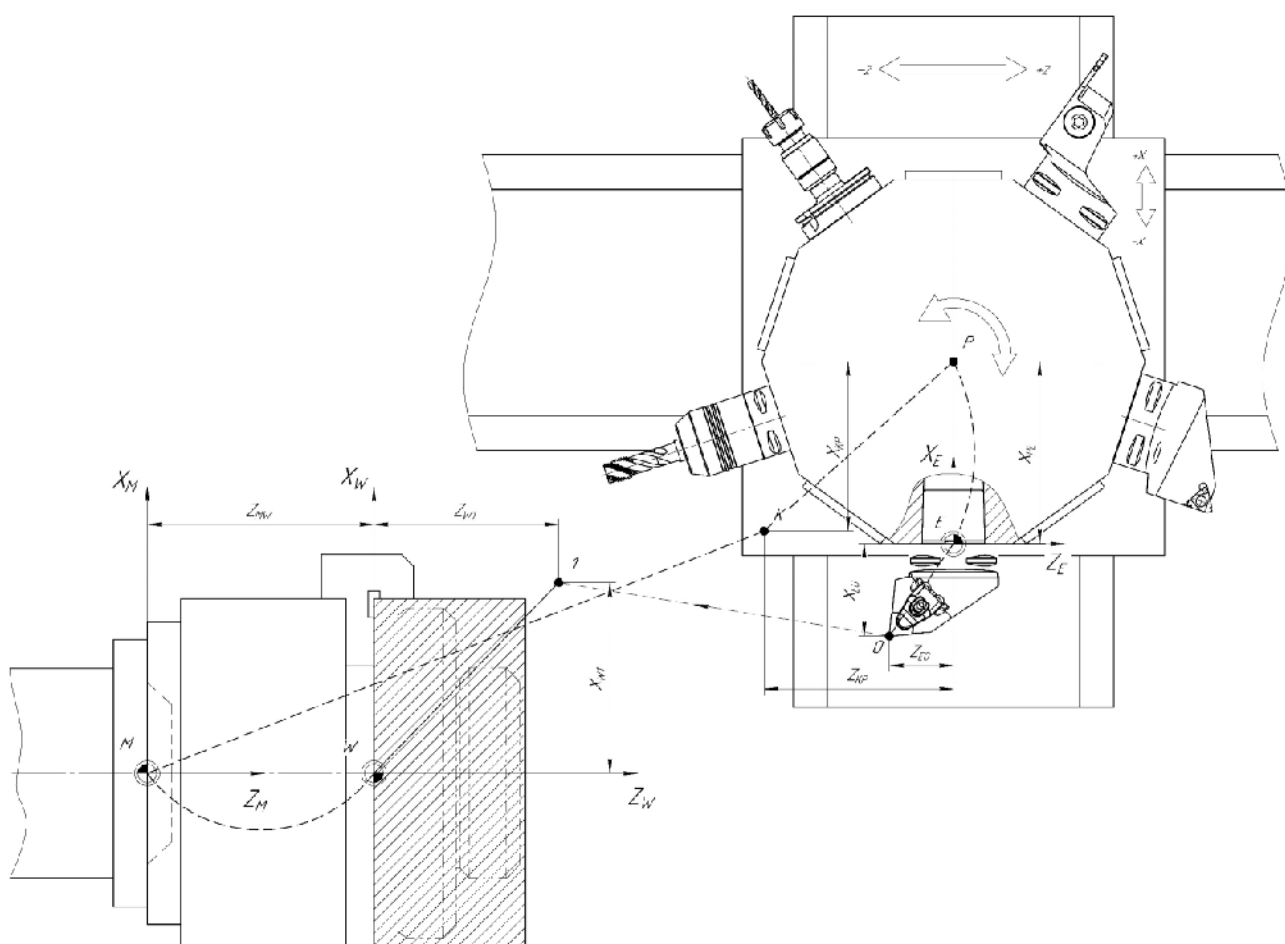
Связь систем координат токарного станка, детали и инструмента
